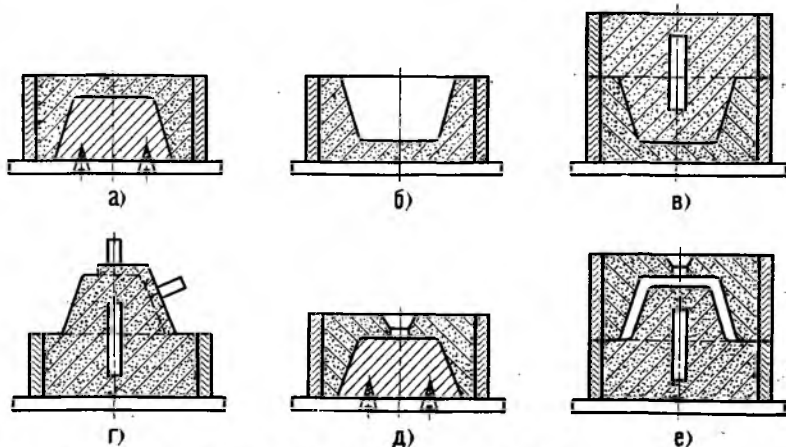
Формовка по гипсовой модели с подрезкой болвана
